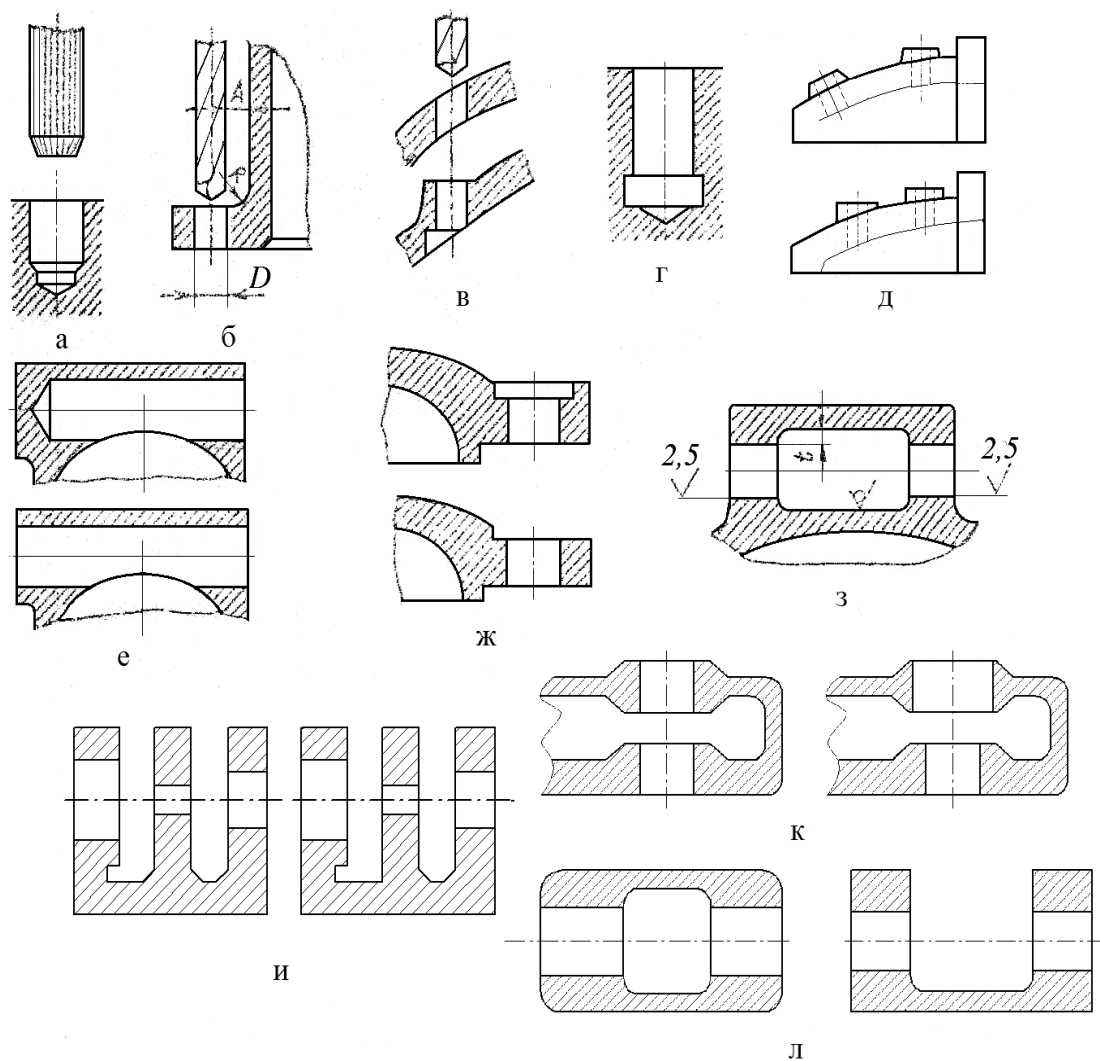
Приклади поліпшення технологічності деталей оброблюваних на свердлильних та розточувальних верстатах
